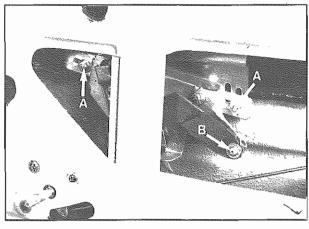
A - Viti fissaggio piastra porta cristallo Glass holder fixing screws
